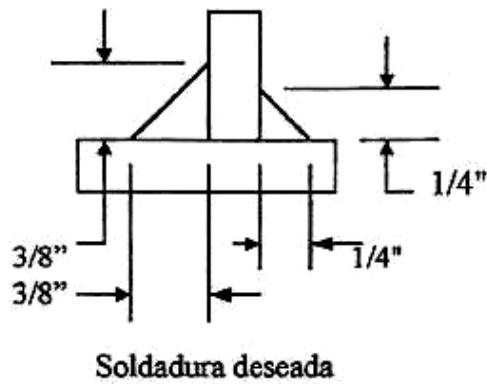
SOLDADURA DE FILETE POR AMBOS LADOS
